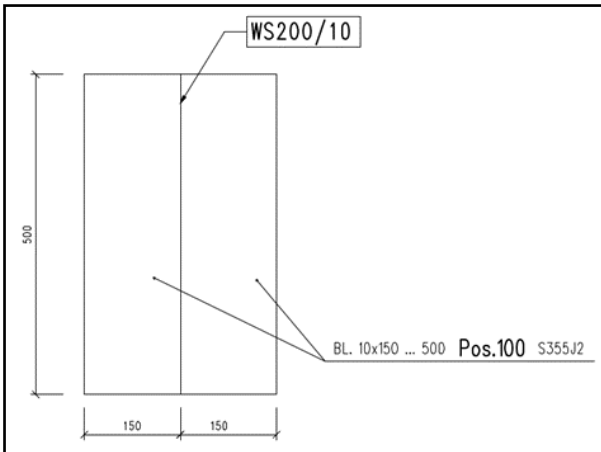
Geometrie der geschweißten Probekörper (Auszug aus dem Werkstattplan)
